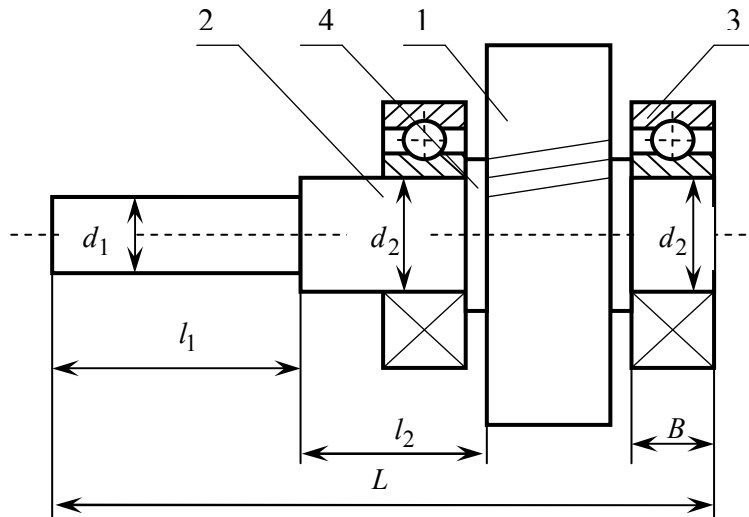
Складальна одиниця вузла обертання механічної передачі: 1 — зубчасте колесо, 2 — вал, 3 — опори валів (підшипники кочення), 4 — розпірна втулка
